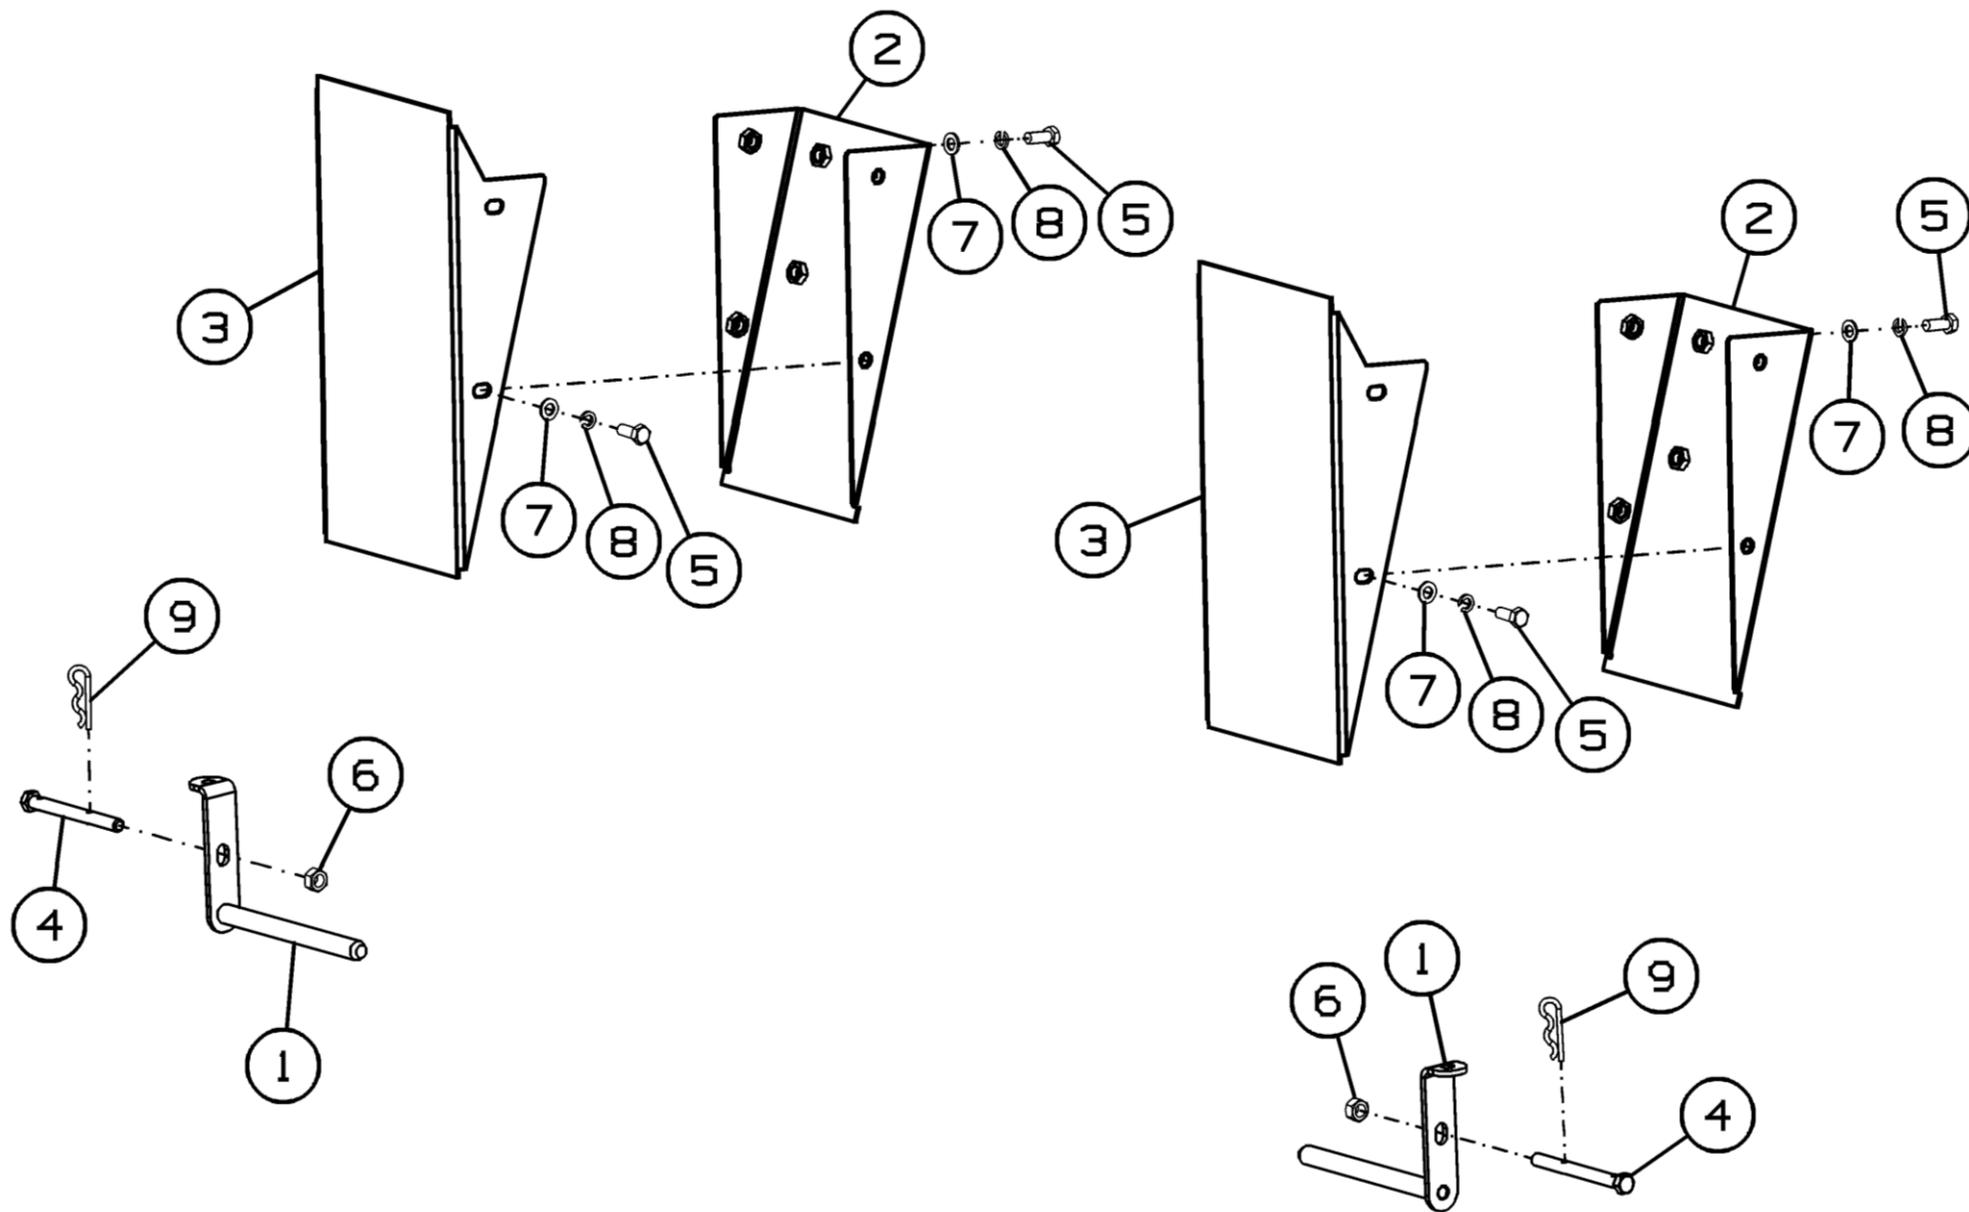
Установка щитков и фиксаторов ППК-122.01.00.500
